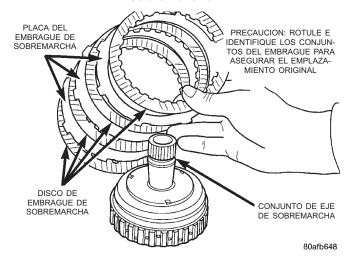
Conjunto del embrague de sobremarcha NOTA: Rotule el conjunto de embrague de sobremarcha a fin de tener una identificación de referencia para cuando vuelva a ensamblar.
